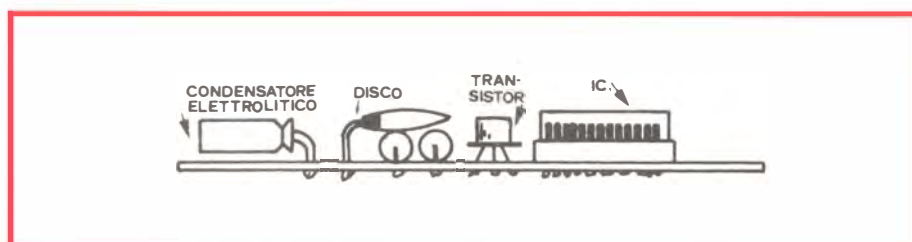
Bassetta stampata tipo a montaggio ultimato e vista in sezione: notare i componenti piegati, anche su altri, per contenere l'altezza del montaggio.
